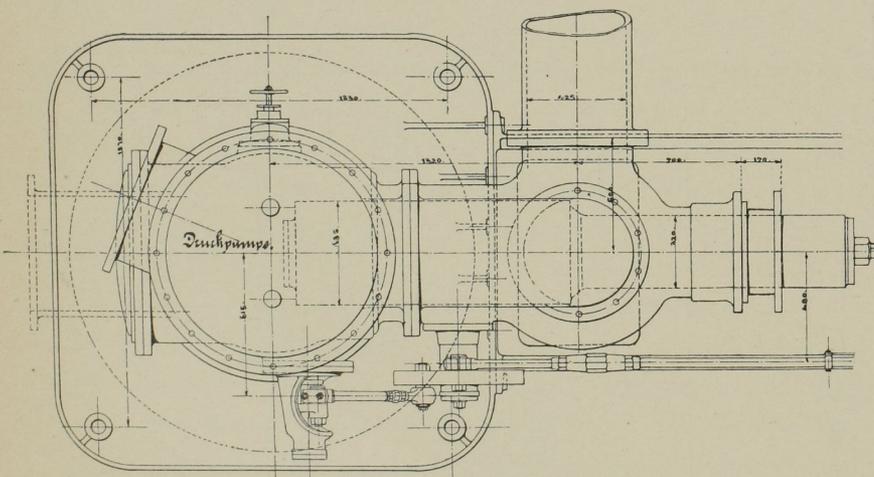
Grundriss der Druckpumpe. Massst. 1:30.
